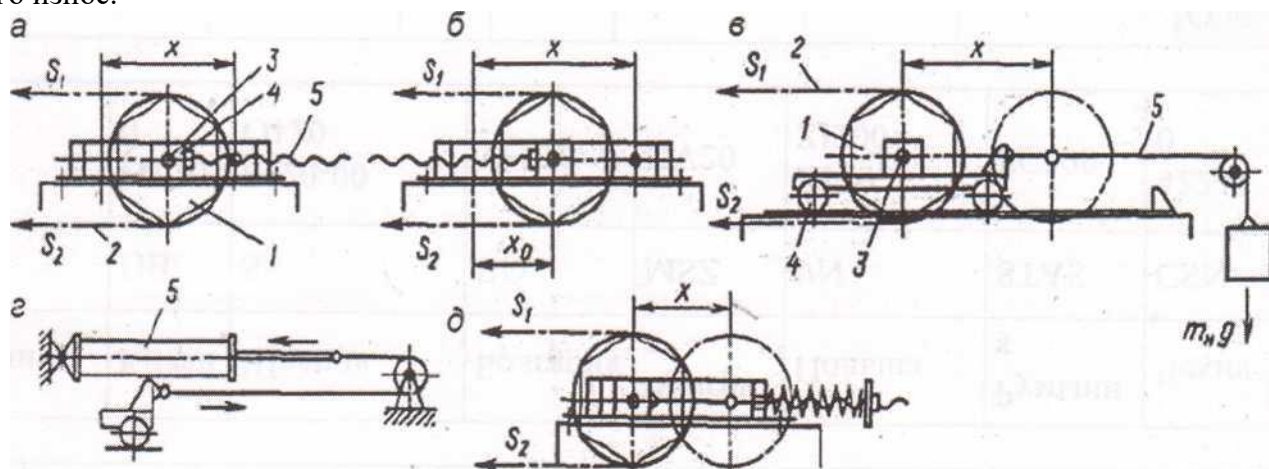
Схемы натяжных устройств: а и б - винтовых; б - тележечного грузового; в - гидравлического (пневматического); д - пружинно-винтового; 1 - поворотное устройство; 2 - тяговый элемент; 3 - ось; 4 - тележка; 5 - натяжной механизм
